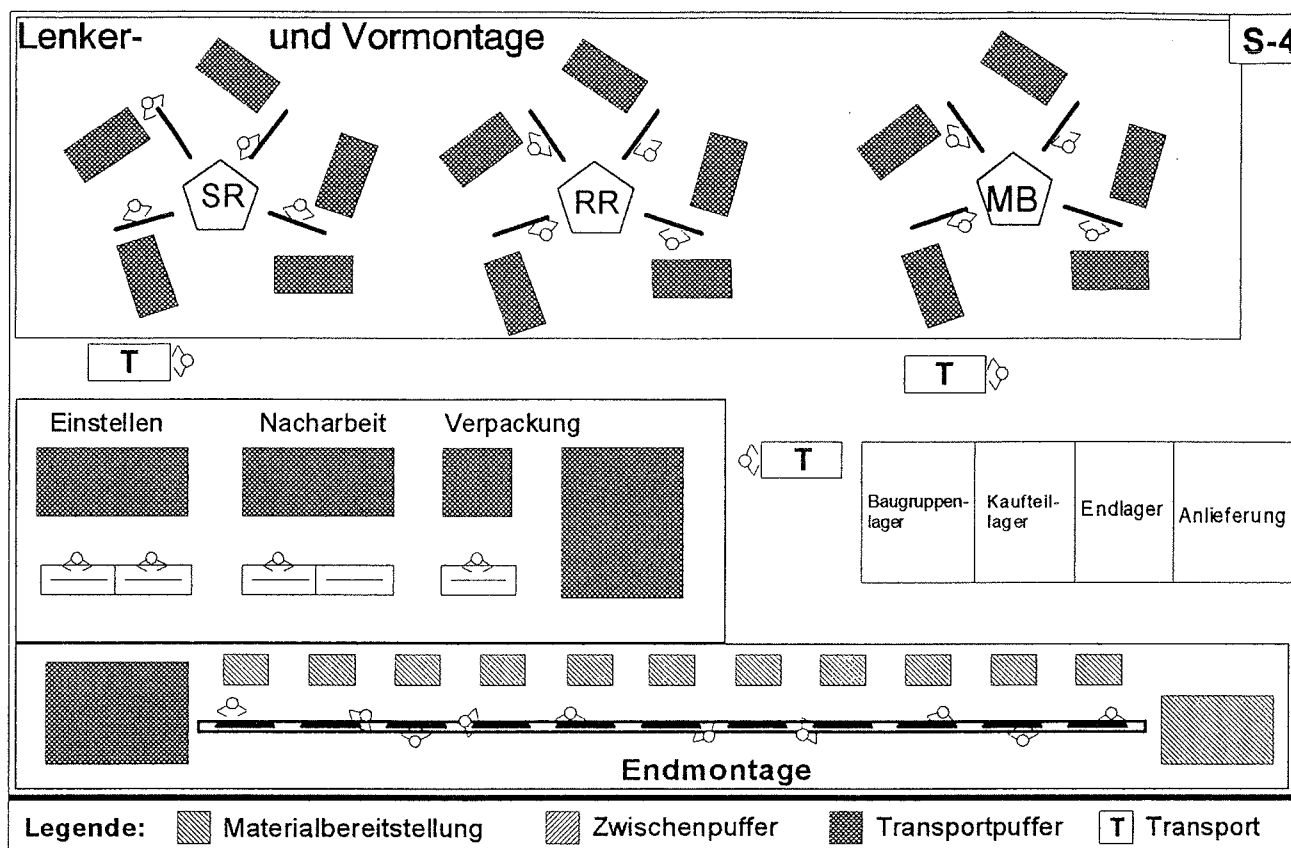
Layout der varianten Fahrradfabrik S-4
